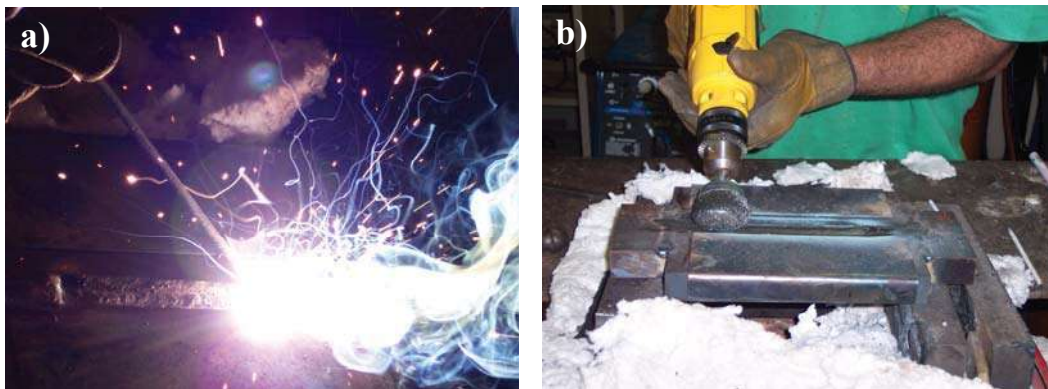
a) Procedimiento de soldadura de recubrimiento con Co-Cr (Stellite); b) Limpieza y acabado final.
